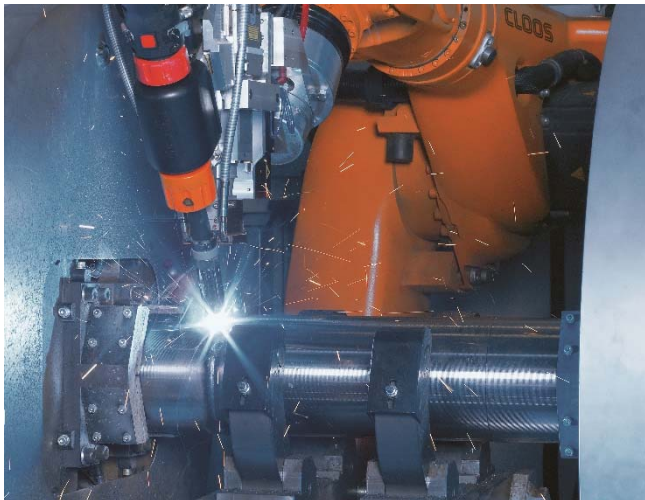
Laserstrahl-MIG-Hybrid-Kopf zum Schweißen von Rundnähten
